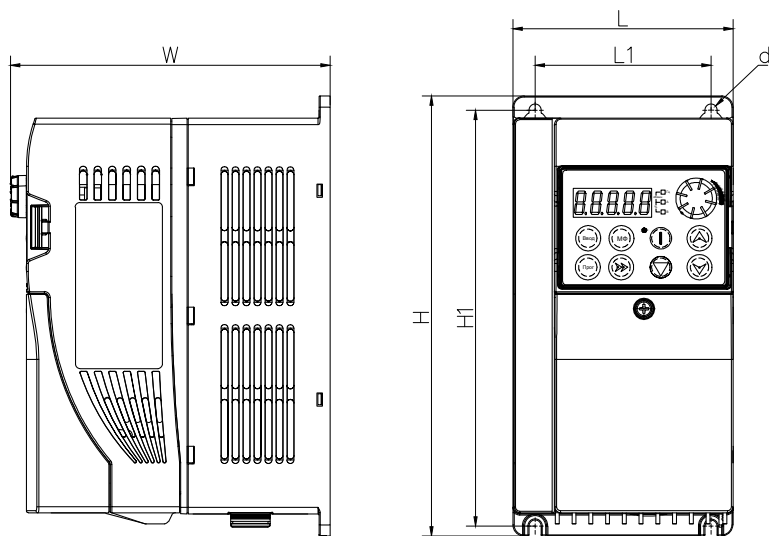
Габаритные и установочные размеры преобразователя (габарит 2)
